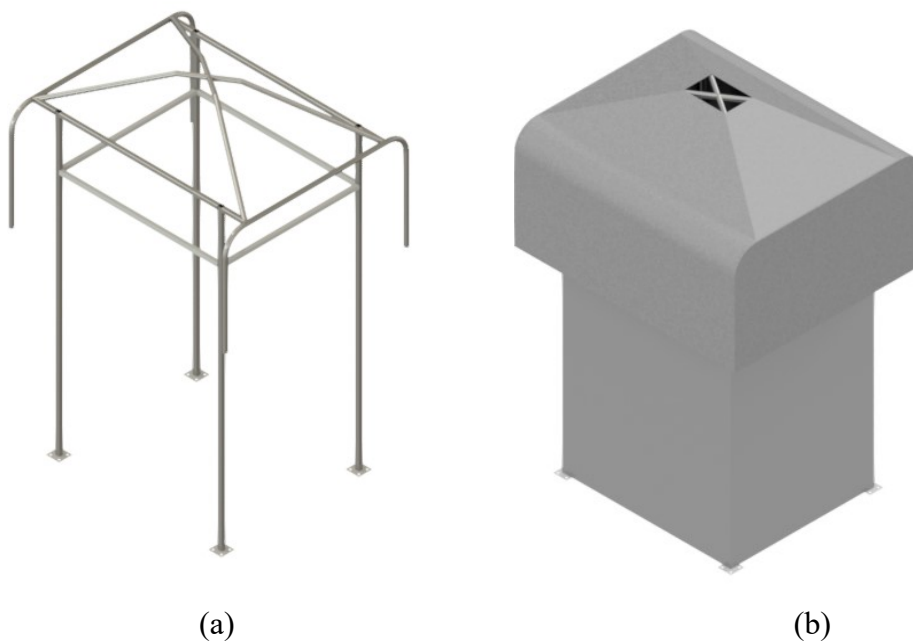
Proteção 2: (a) estrutura em aço; (b) manta sobre a estrutura em aço.
